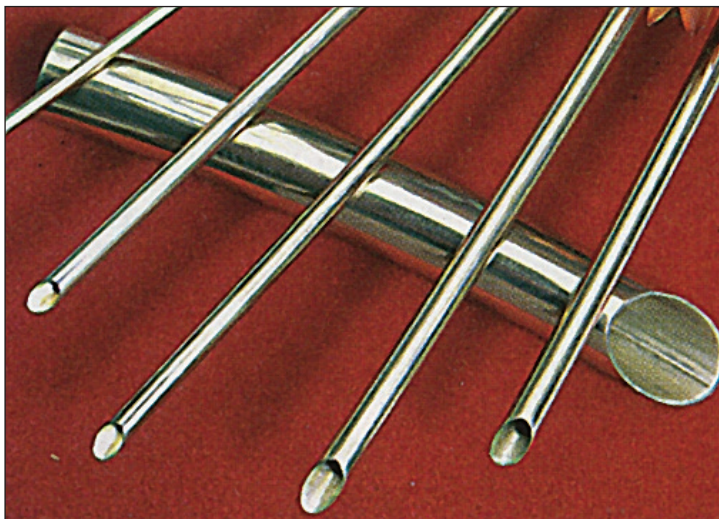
Образцы сварных трубок диаметром от 5 до 25 мм
